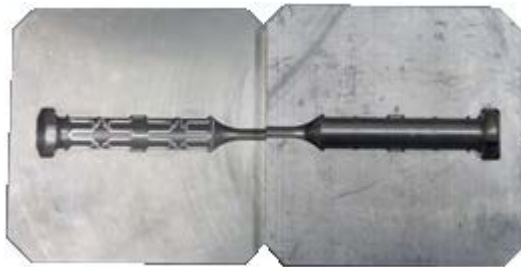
Insertos usinados em alumínio junto com o núcleo.
